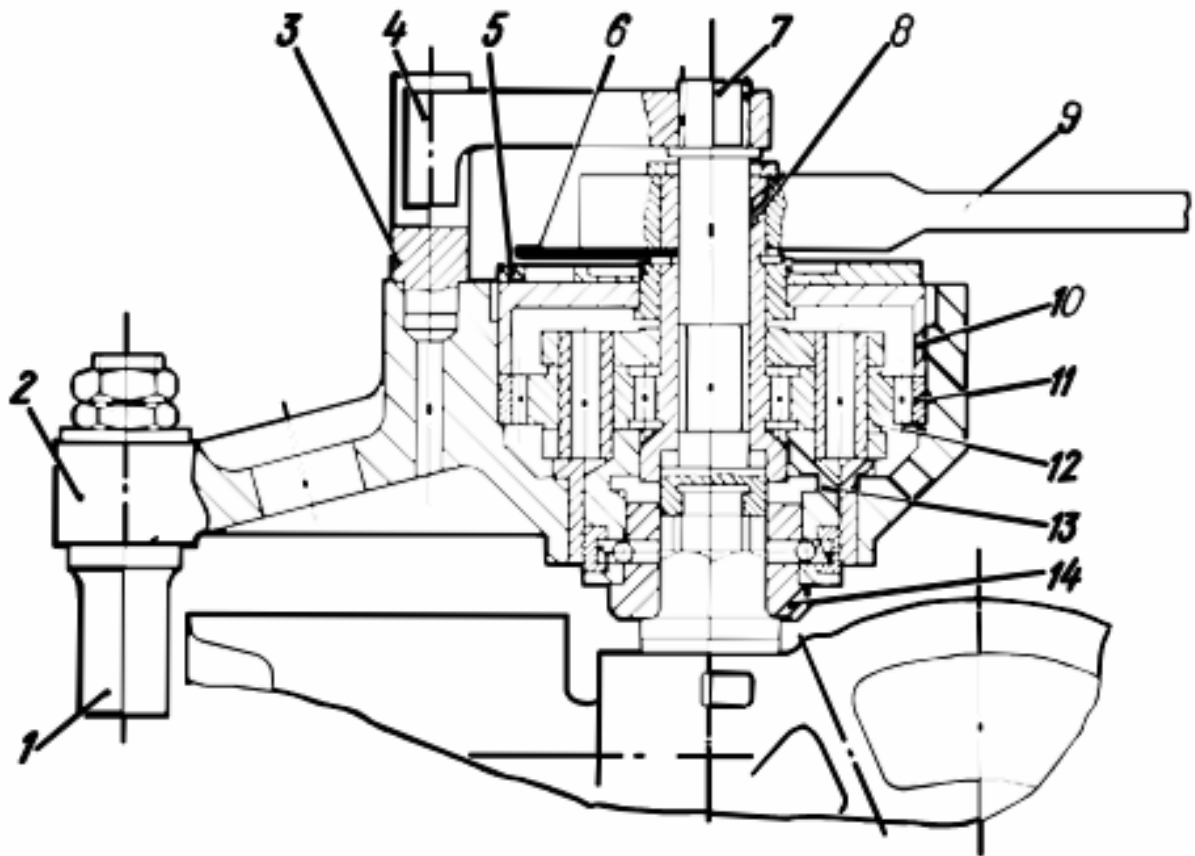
Ключ 96830-1554 для затяжки гаек крепления крышек коренных подшипников:
